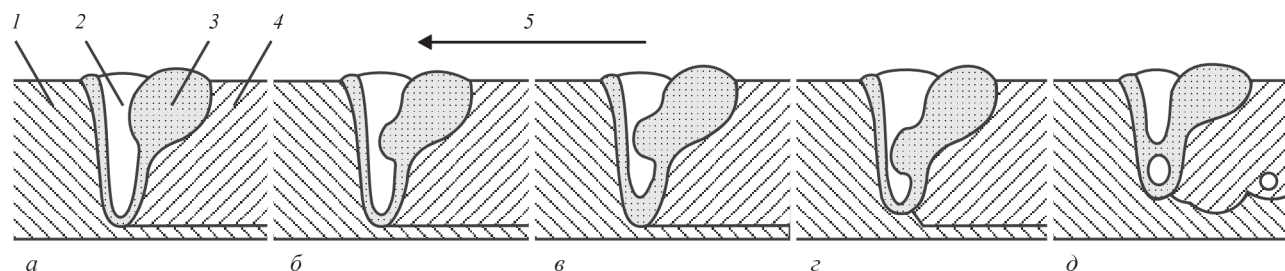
Схема формирования пористости внутри ванны расплава трека, выполненного с параметрами глубокого проплавления [18] (а–д — соответствуют опытным образцам № 1–5): 1 — подложка; 2 — лунка; 3 — расплав; 4 — сплавленный трек; 5 — направление движения лазера
